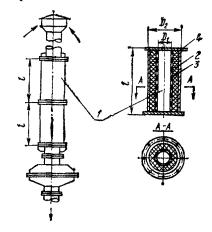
Схема трубчатого глушителя шума на всасывании воздуха компрессорных установок
